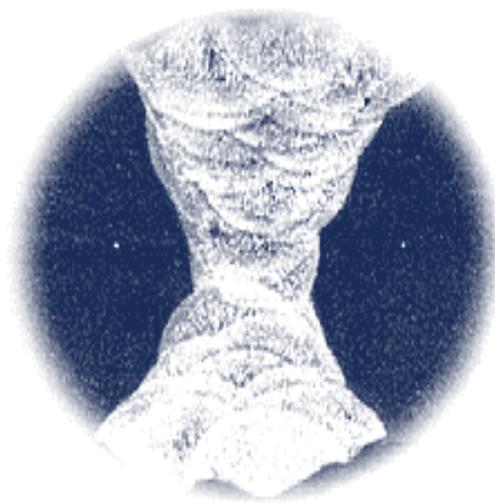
Macro 3X de soldadura húmeda y propiedades del metal soldado.
